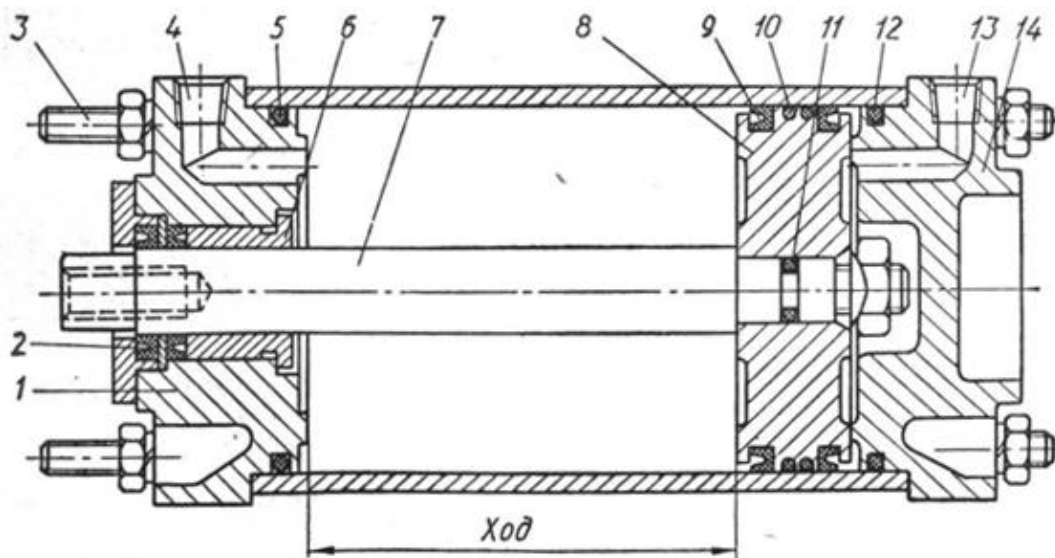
Конструкция поршневого пневмоцилиндра двухстороннего действия
